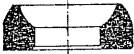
Kamień łozyskowy - oprawiający - oski minutowej.
